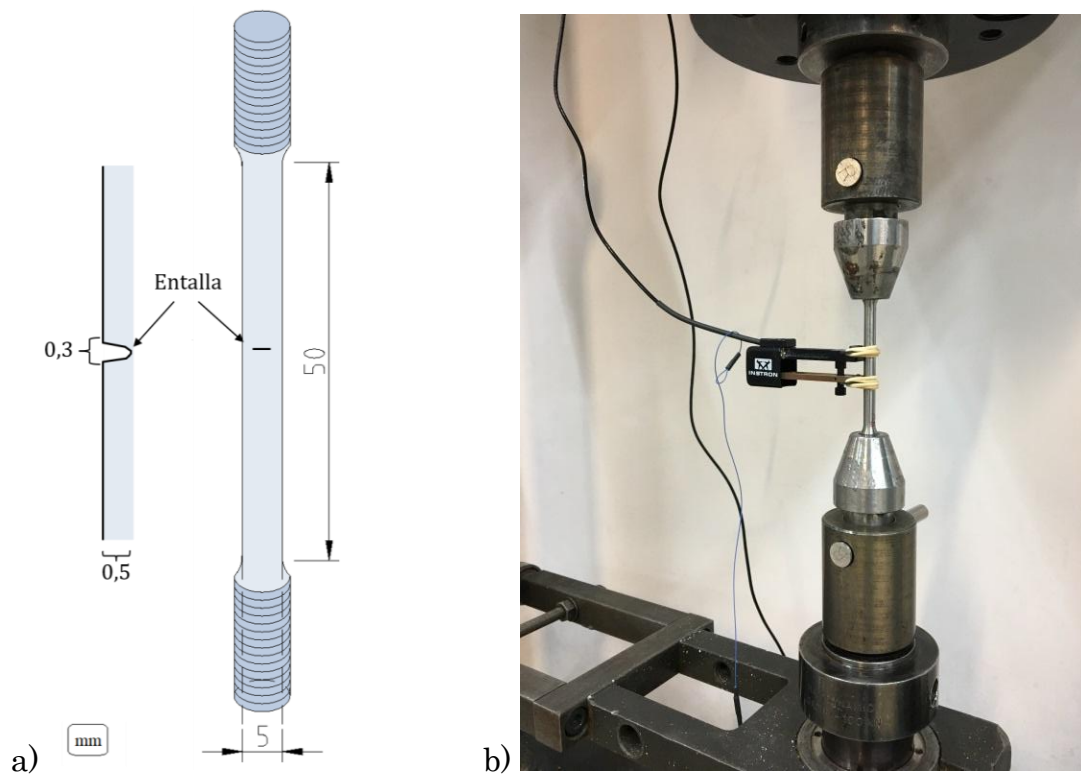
a) Configuración y dimensiones de las probetas cilíndricas empleadas para medir la tenacidad; b) Montaje del ensayo
